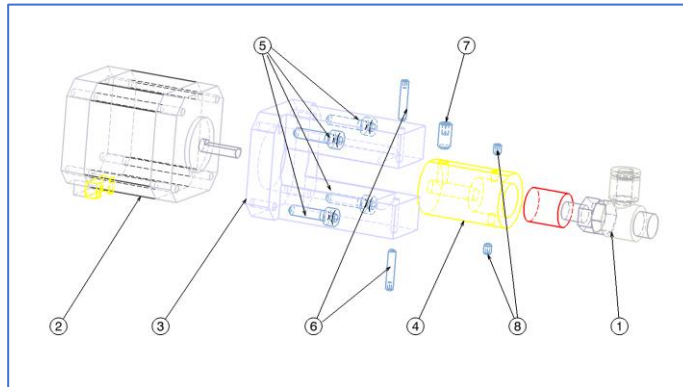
Vedere din desenul de execuție explodată realizată în CATIA
